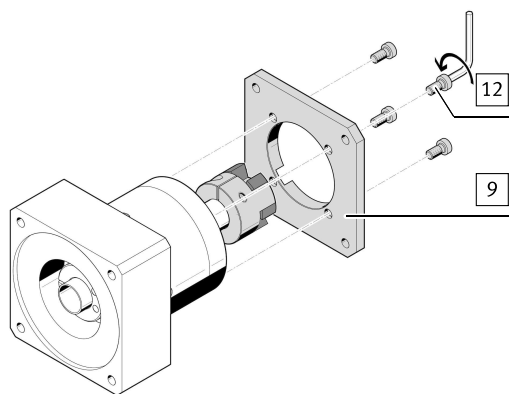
Крепление фланца мотора, на стороне редуктора – Вариант G
